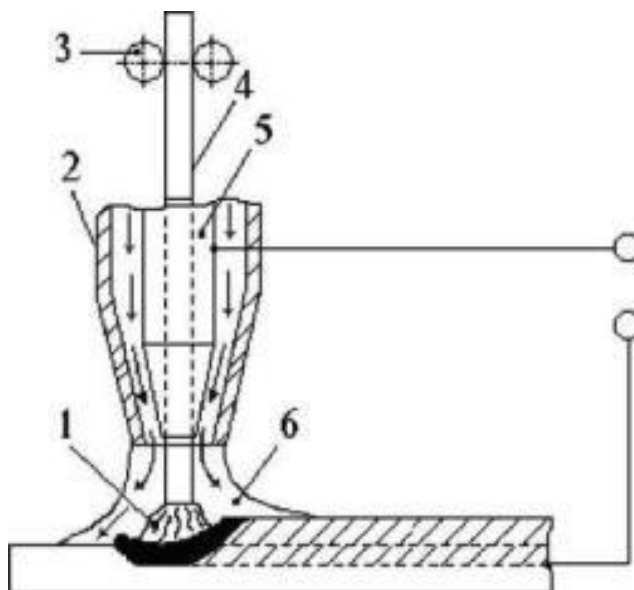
Схема дуговой сварки в среде защитных газов:
